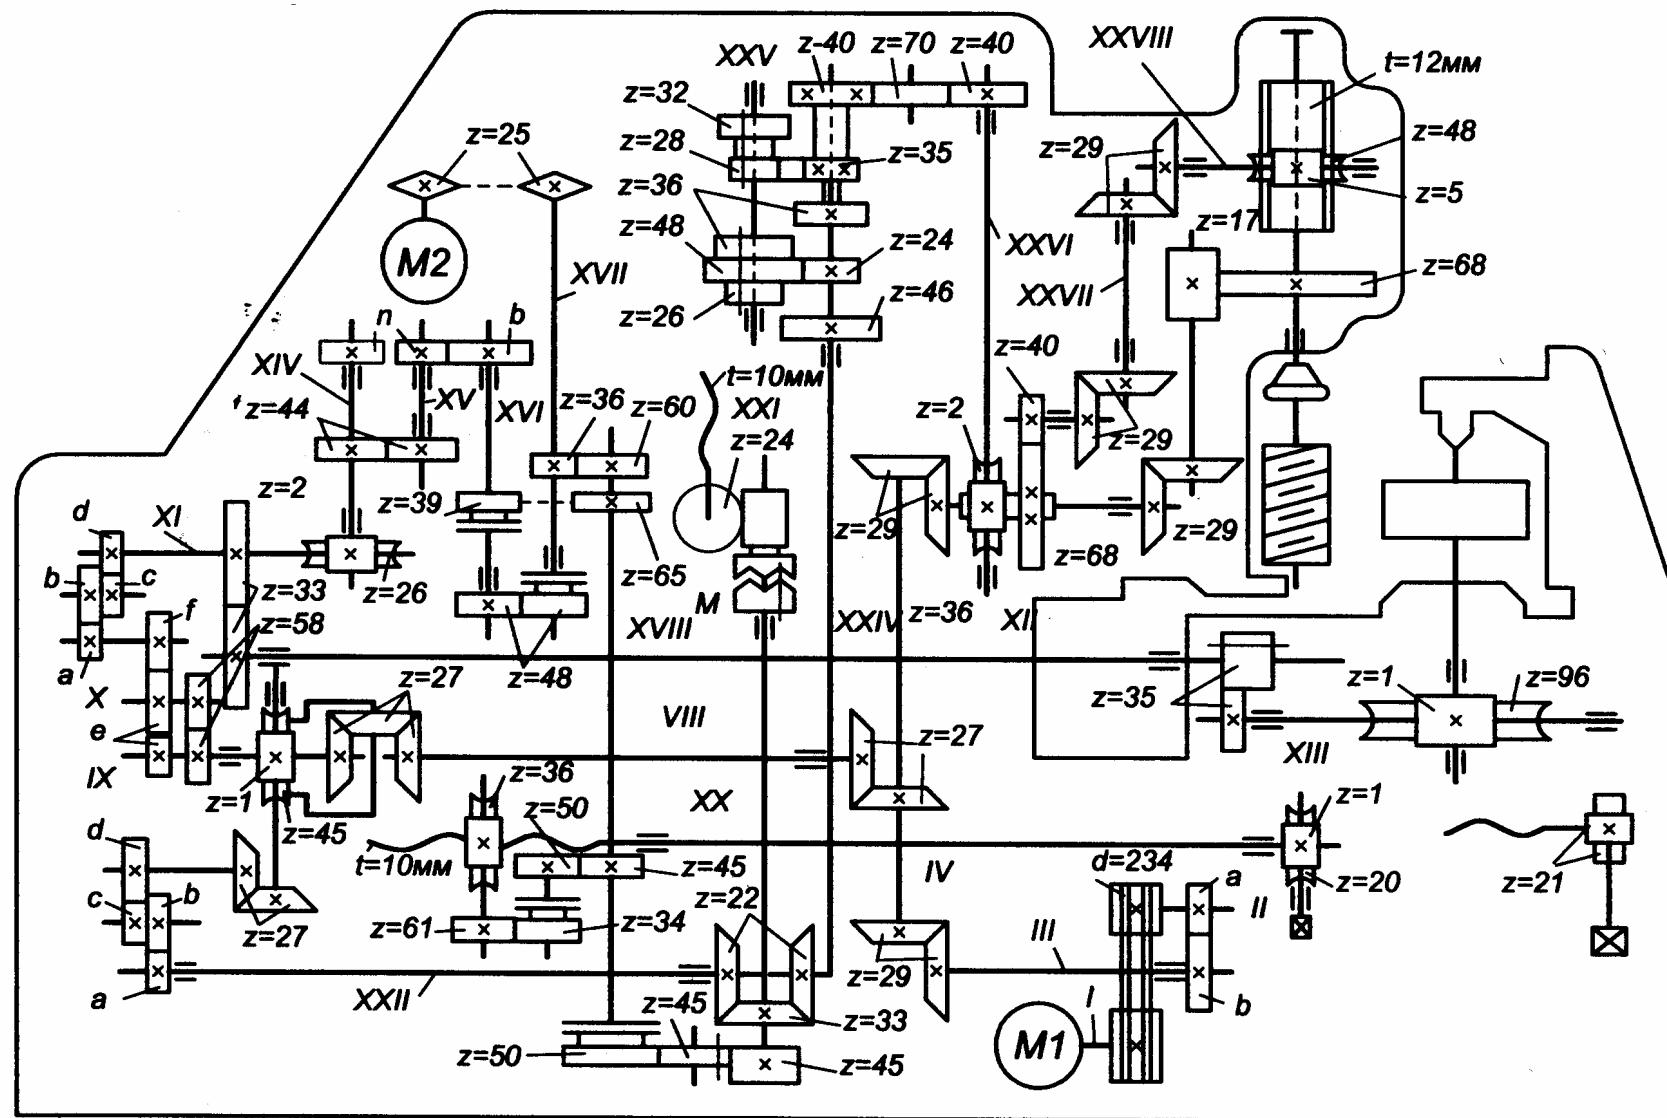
Кинематическая схема зубоффрезерного станка мод. 5К32
